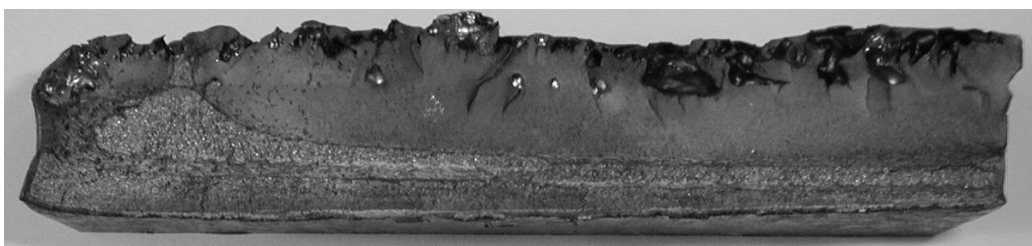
Macrografia da superfície de fractura do provete PDR7.
